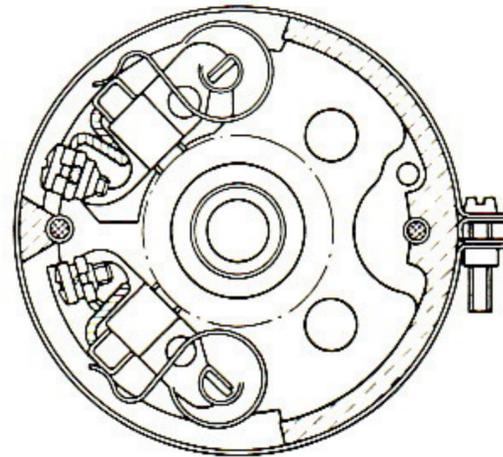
Sezione sul supporto lato collettore con vista delle spazzole.
